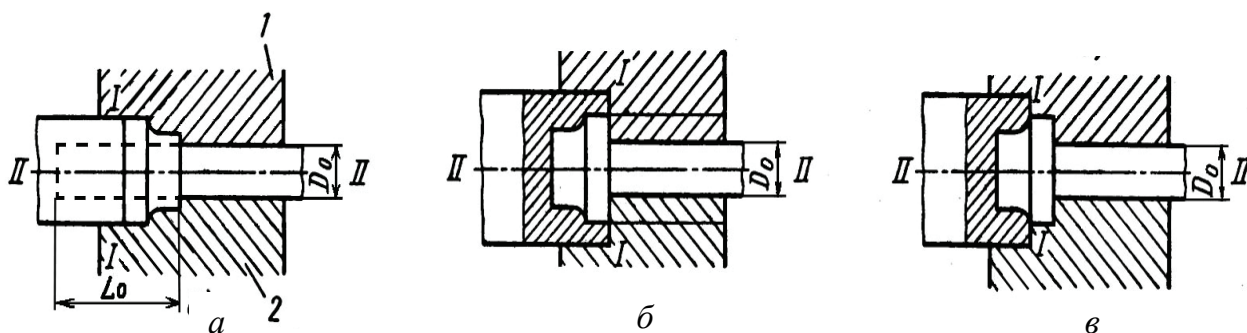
Схемы расположения поковки в штампах (горизонтальный разрез штампов вид сверху):
